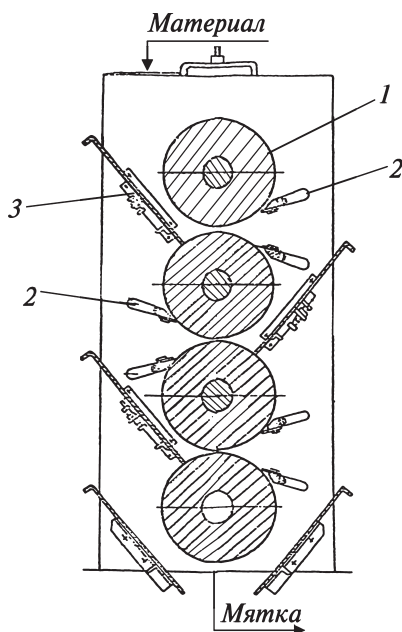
Схема работы вальцового станка Б6-МВА-М:
